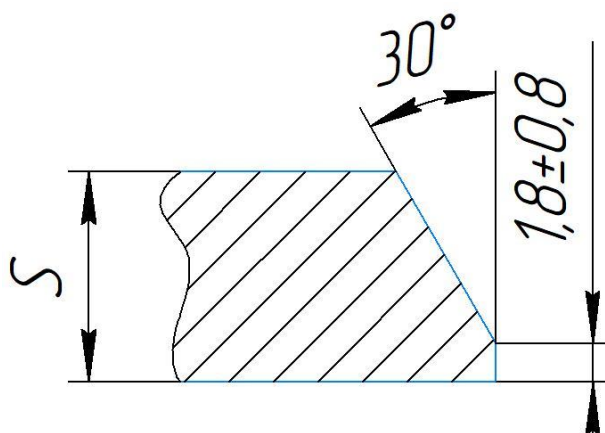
Геометрические параметры заводской разделки кромок торцов труб для сборки под сварку трубы с толщиной стенки (S) до 15,0 мм включительно [8]
